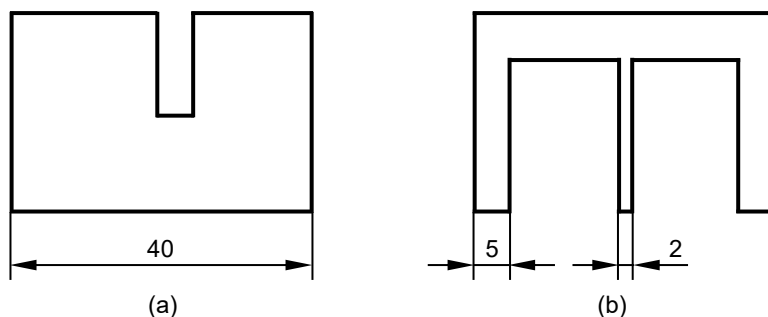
Exemplos de colocação de cotas interior e exteriormente às linhas de chamada.
